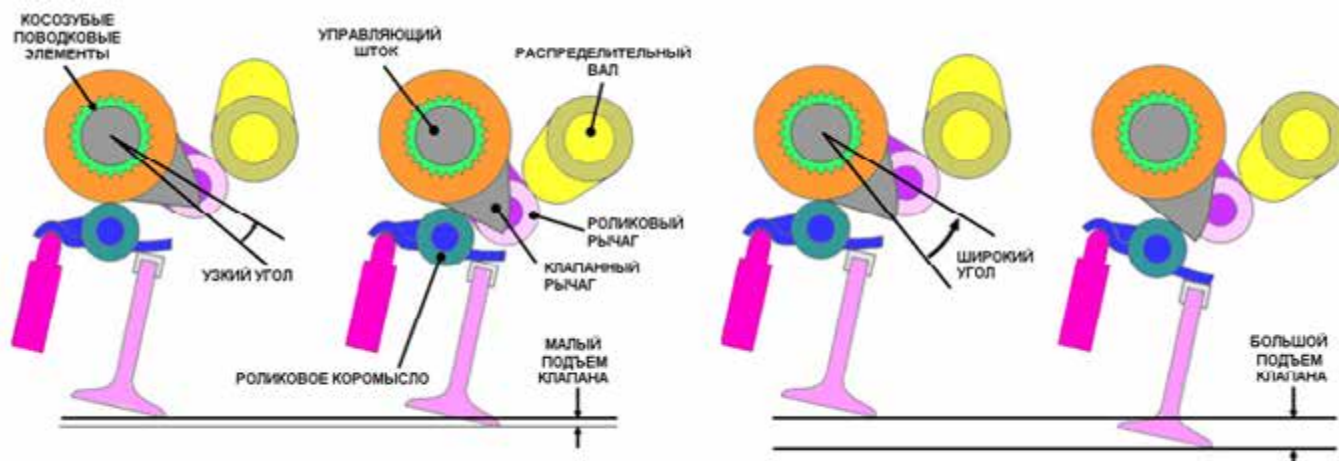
Изменение углового положения роликового рычага относительно клапанного рычага вызывает изменение подъема (хода) клапана при воздействии на этот механизм кулачка распределительного вала; источник: Toyota
